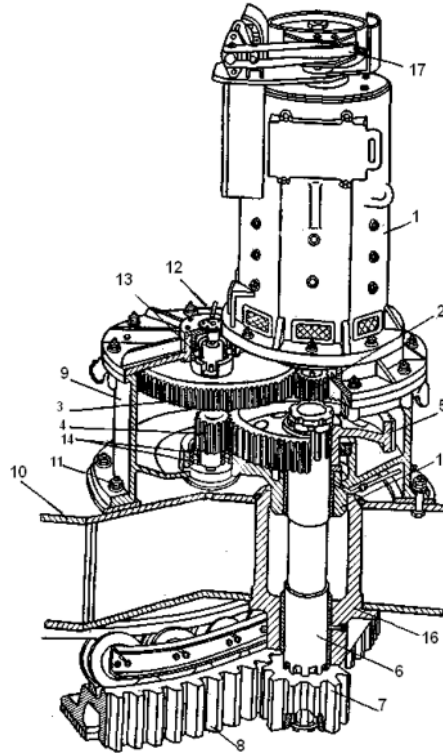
Механізм повороту екскаватора ЕКГ-8І:
